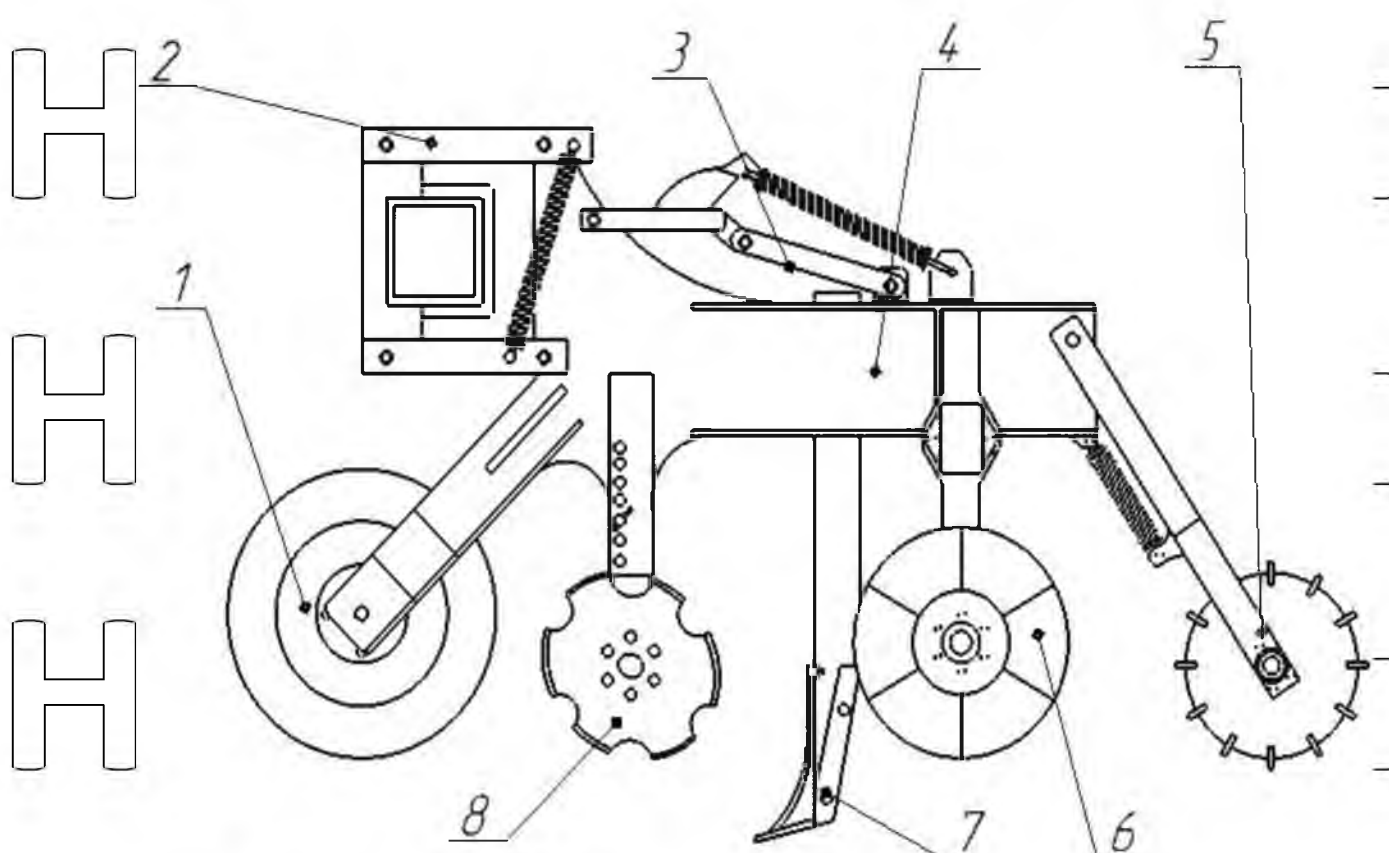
Культиватор Stripcat для стрічкового обробітку ґрунту:
